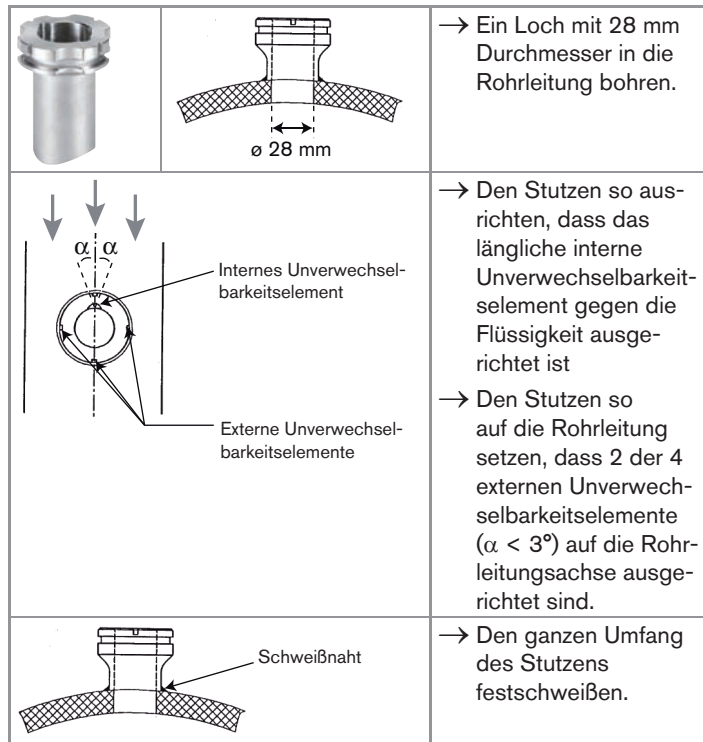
Installation eines Schweißstutzens aus Metall
